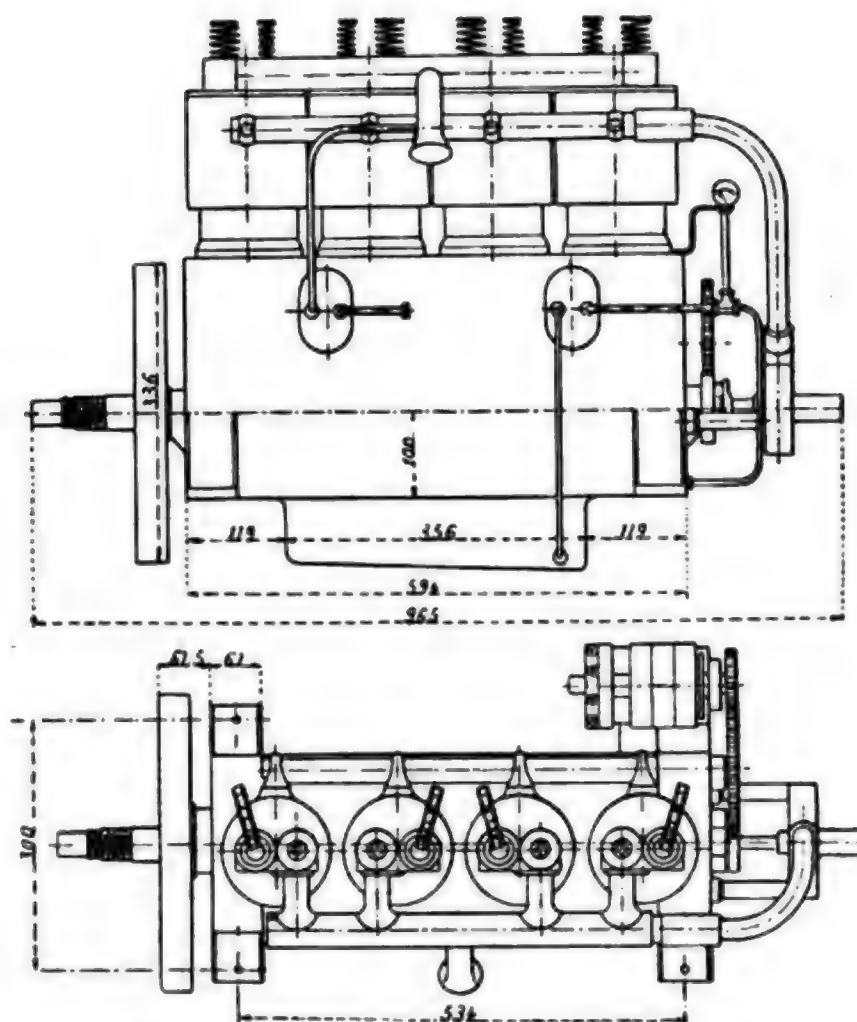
und 267. Zeichnung des Flugmotors, System Wright, Seitenansicht und Ansicht von oben.
